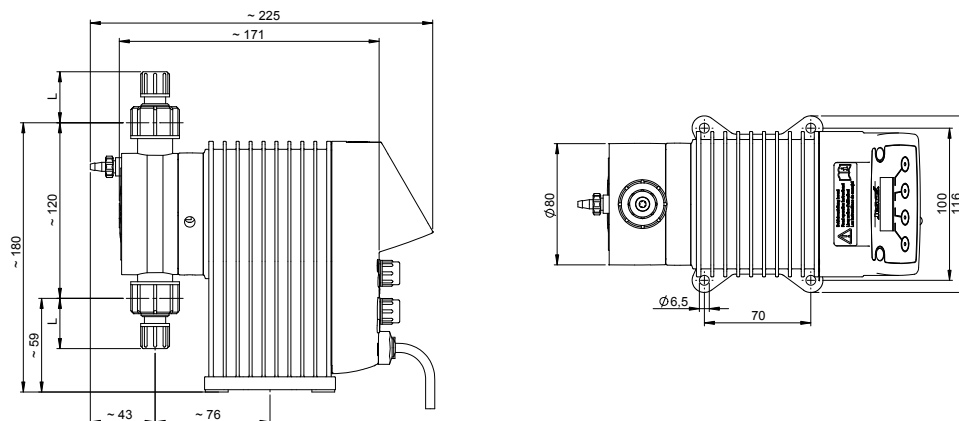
Габаритный чертеж MAGDOS LA / LD с дозирующей головкой из ПВХ, ПП или ПВДФ (все размеры в мм)
